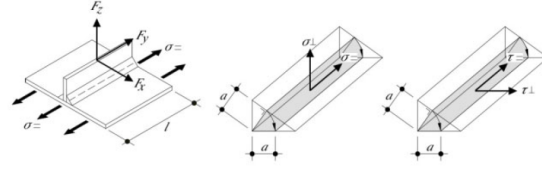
Tensões atuantes em soldaduras, adaptado de [19]
